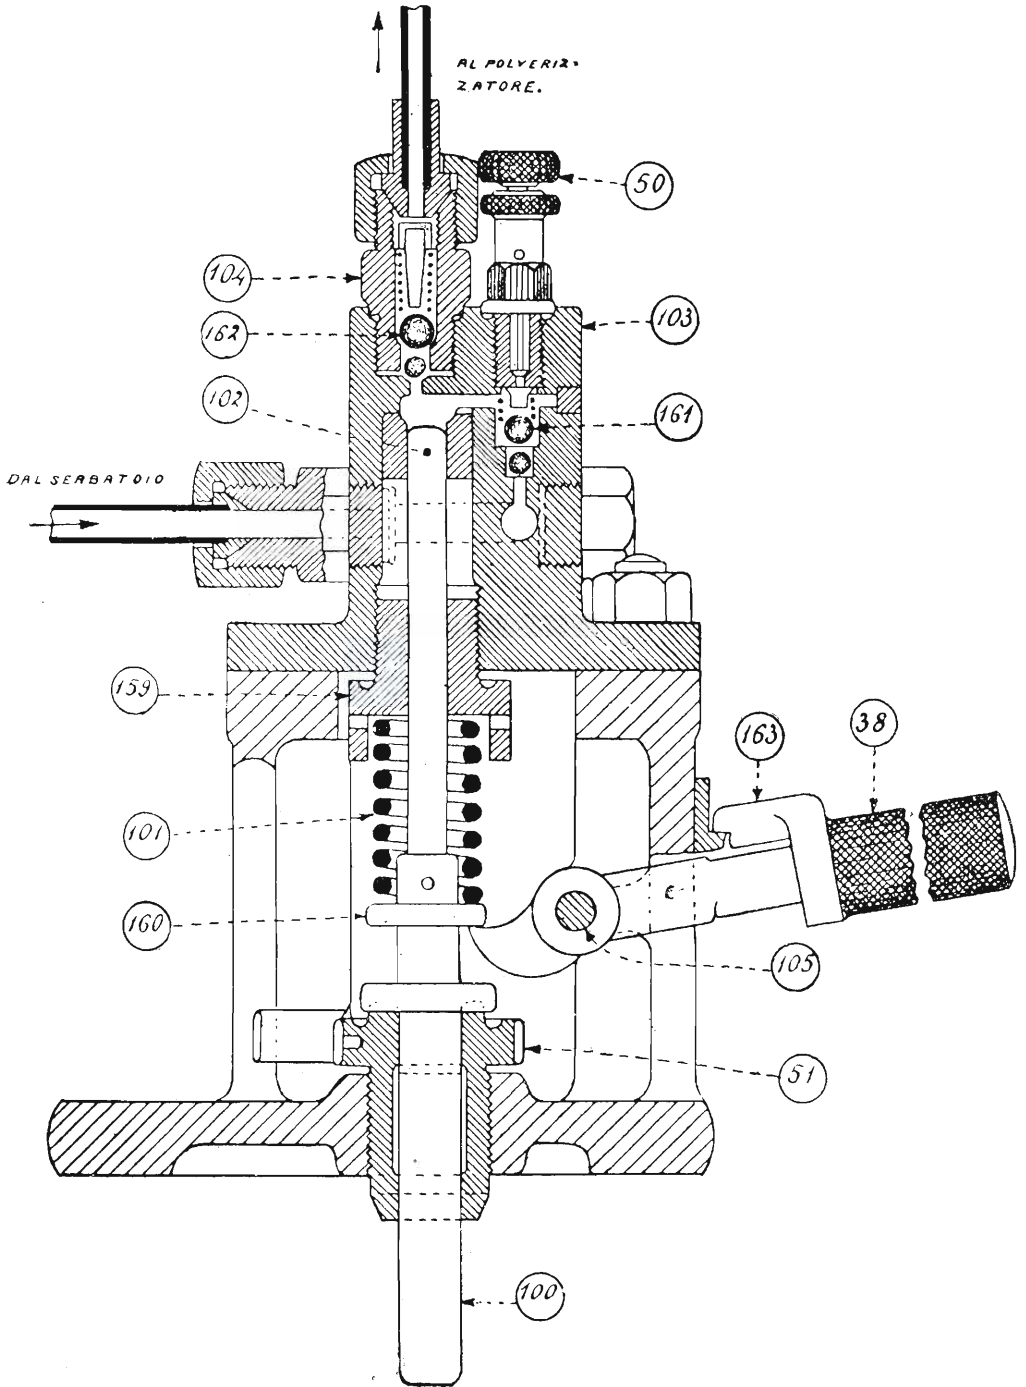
Motore a testa calda S. Giorgio da 18 KW.
